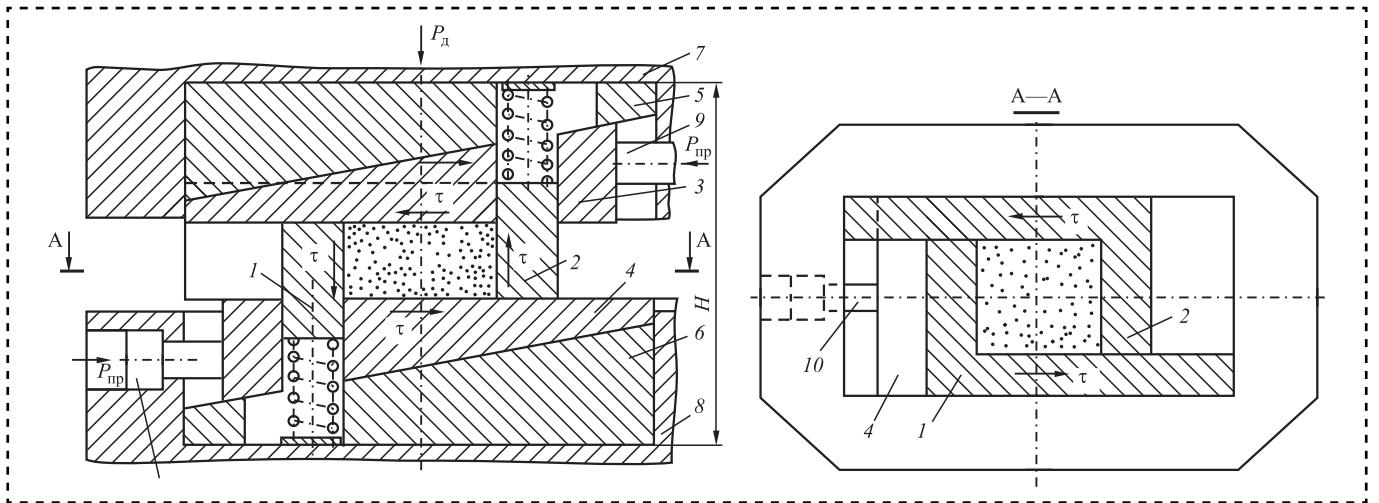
Схема пресс-формы для прессования с раздацией заготовок [4]:
